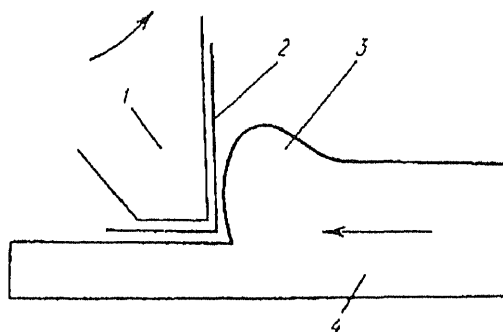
Образование медной пленки в процессе резания металлов: 1 — фреза; 2 — медная пленка; 3 — стружка; 4 — обрабатываемая деталь
